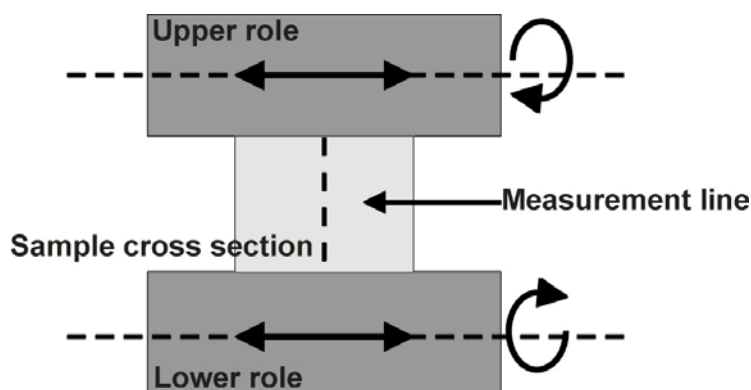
Схема процесса прокатки с дополнительным осциллирующим горизонтальным движением валков
